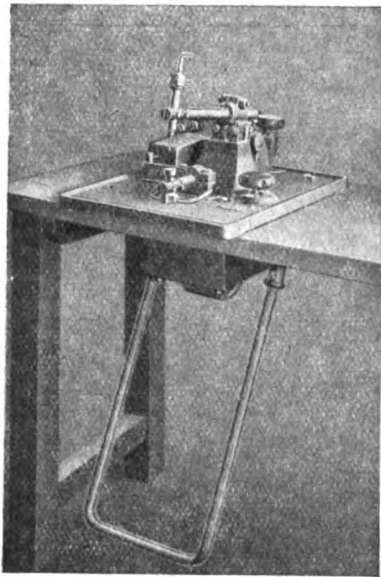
Elektrische Tisch-Punkt-schweißmaschine.
